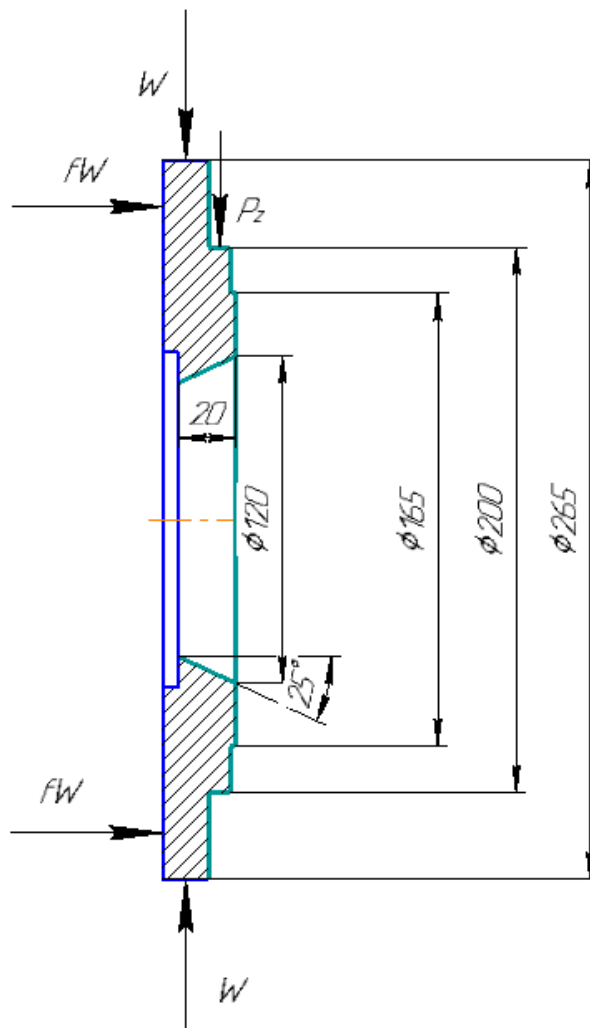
Система сил, що діють на деталь у процесі обробки
